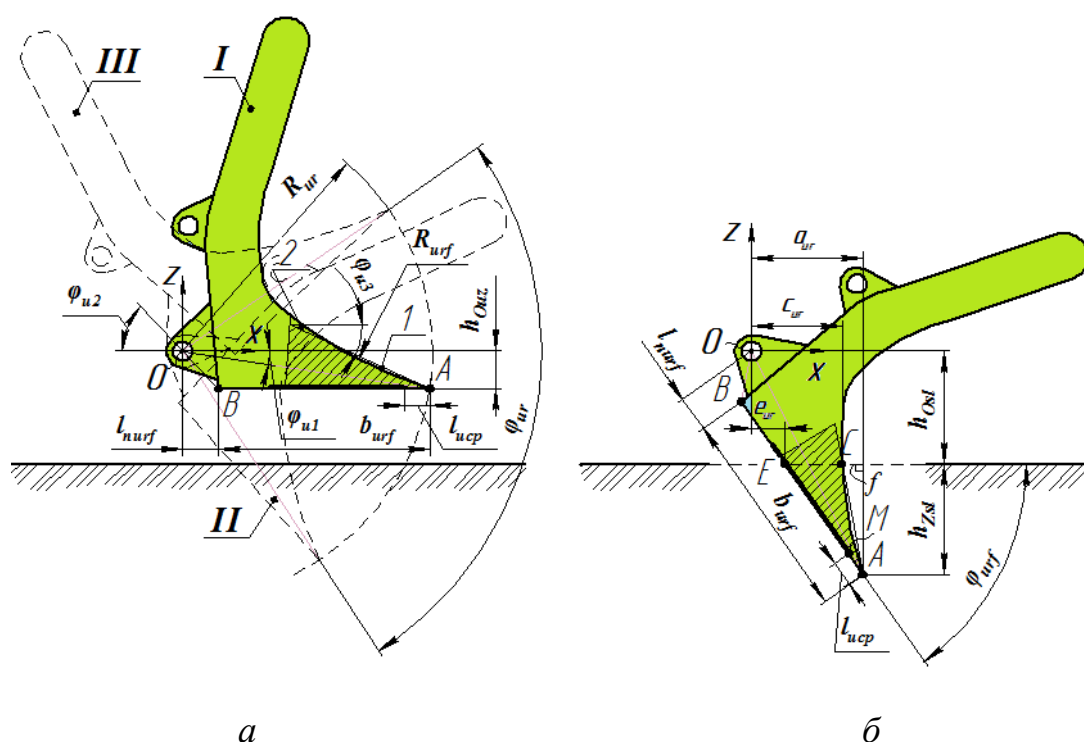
Расчётная схема корчующего клыка корчевателя [рисунок авторов]
